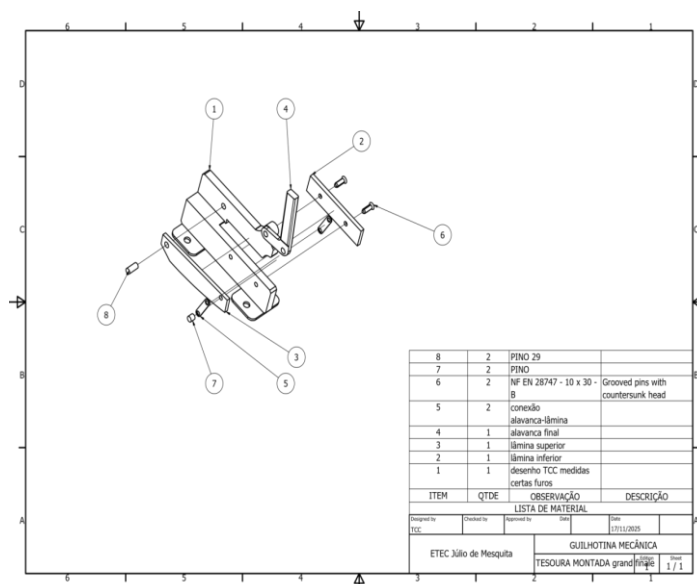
Vista explodida do desenho técnico elaborado no autodesk inventor.
